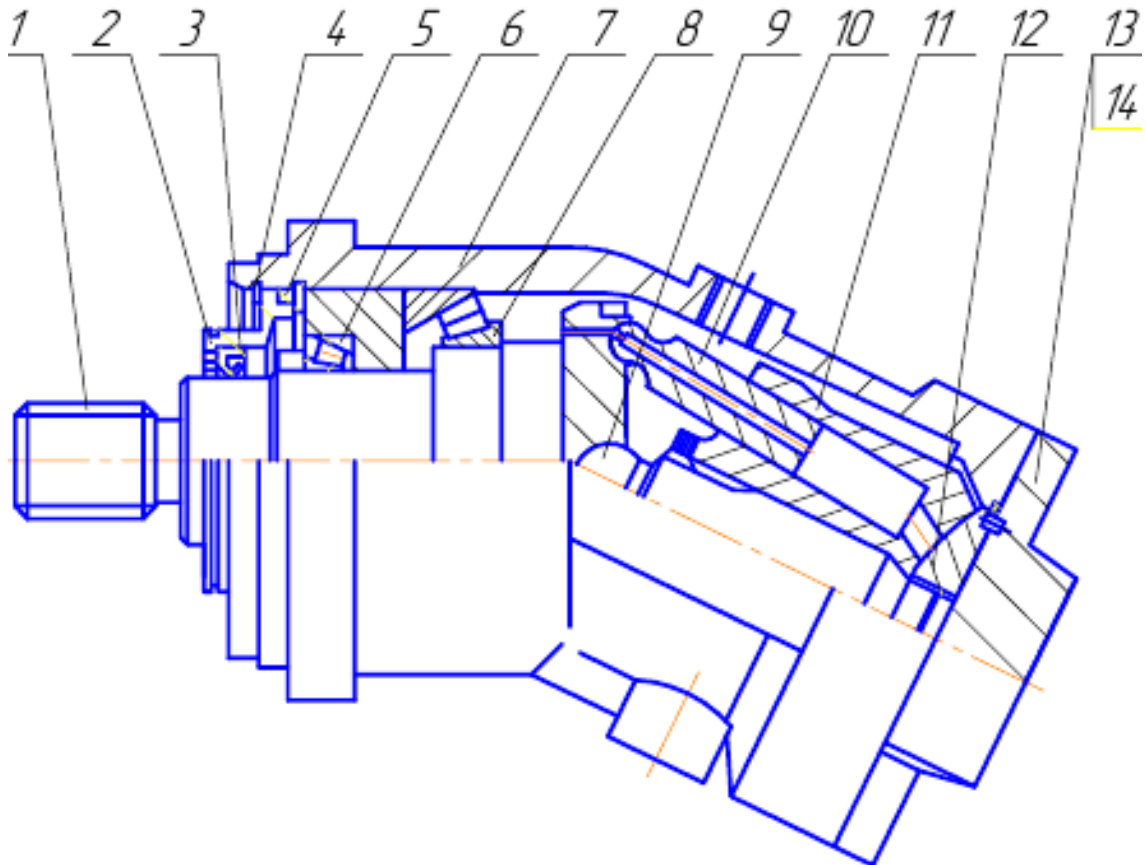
Аксиально – поршневой насос. 1 – вал приводной, 2 – крышка, 3 – манжета, 4 – кольцо стопорное, 5 – кольцо резиновое, 6 – подшипник, 7 – корпус, 8 – подшипник, 9 – шип, 10 – поршень, 11 – блок цилиндров, 12 – распределитель, 13 – кольцо резиновое, 14 – крышка.
